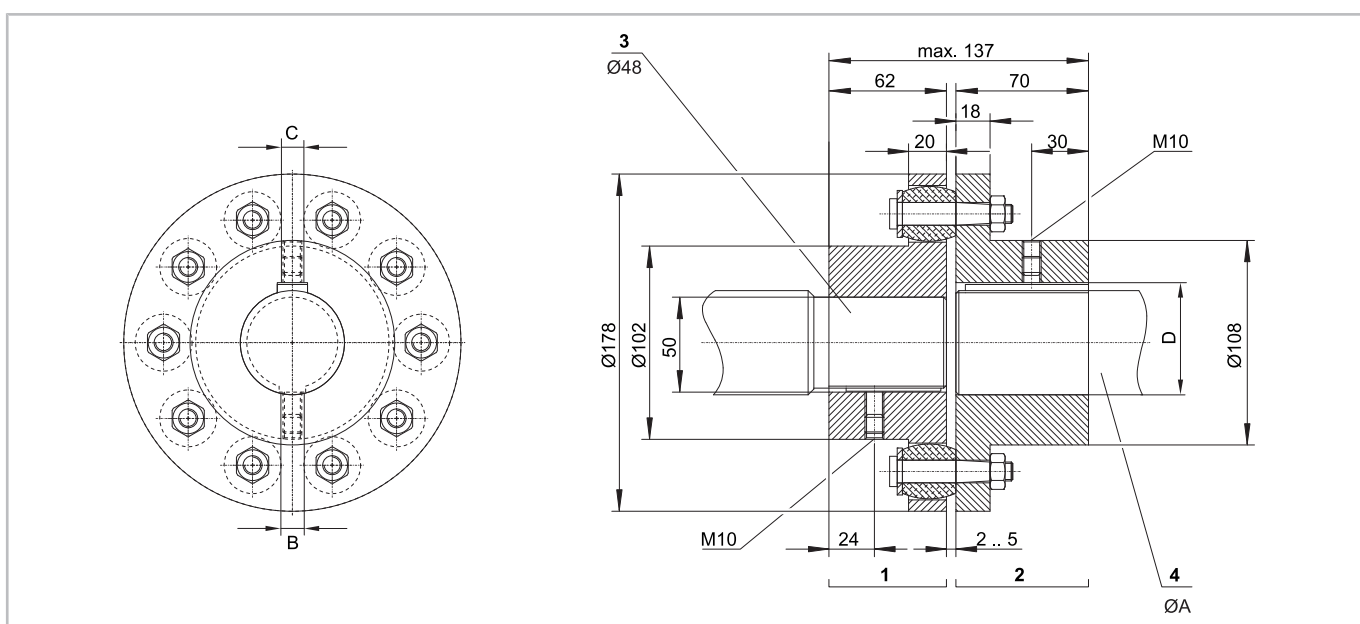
Габаритный чертеж муфты KS730 включая KS730EX
